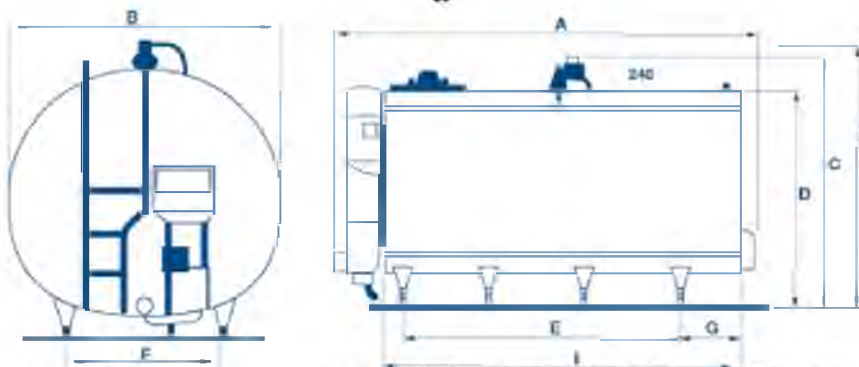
Загальний вигляд (а) та конструктивна схема (б) танка-охолодника
